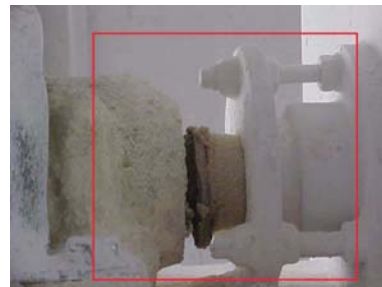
ELEVADOR/EC-2102. Falta resguardo de protección.
